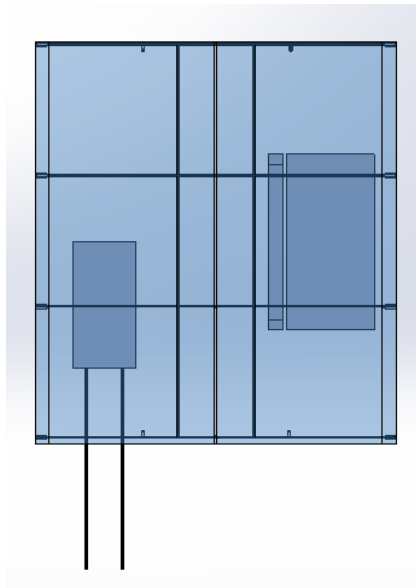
Vista Planta de la disposición de las máquinas en el predio. Fuente: Medidas sacadas del taller de corte de Torres Americanas S.A. Dibujo elaborado por software CAD.
